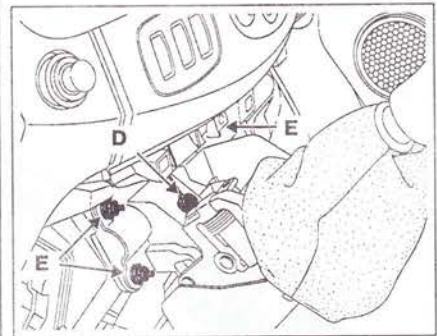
Открутите болт D крепления корпуса рычага переключения передач и три гайки E крепления корпуса рычага переключения передач.
